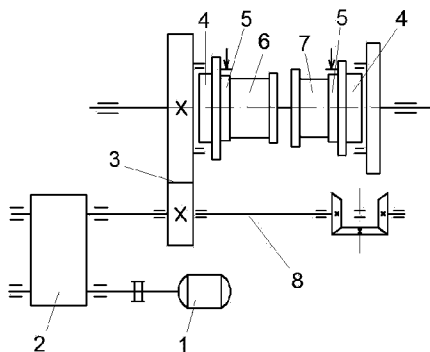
Кинематическая цепь привода главной лебедки подъема ковша:
